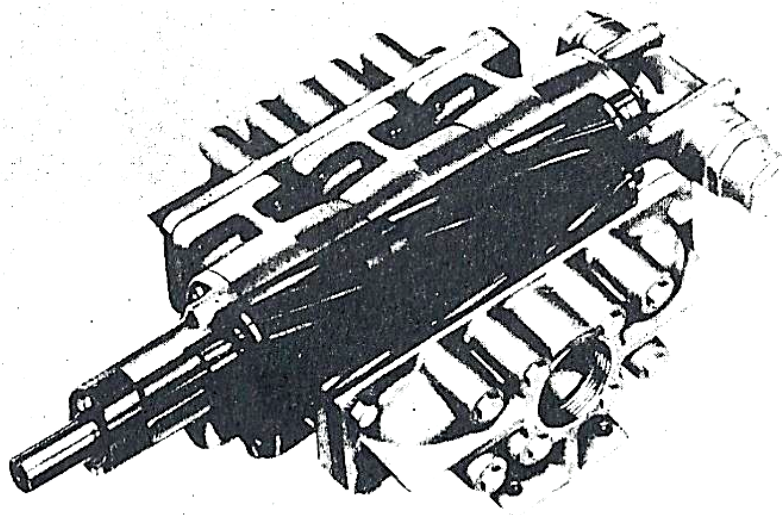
Vistas em corte de bomba de engrenagens de helicoidais.
